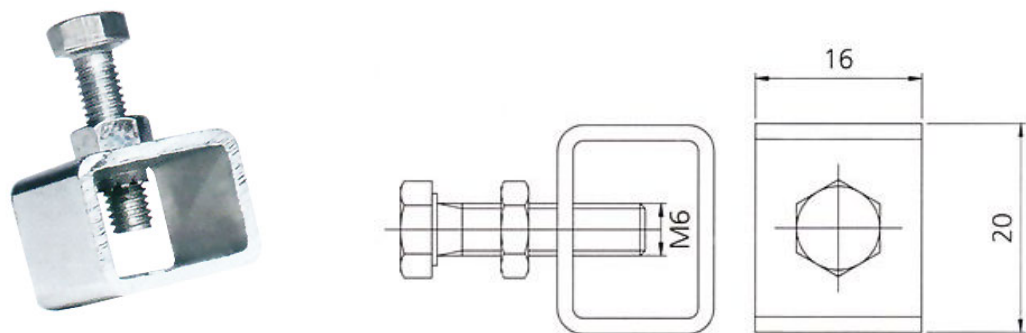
Общий вид стыковочного зажима для коробов с непрерывной медной полосой.
